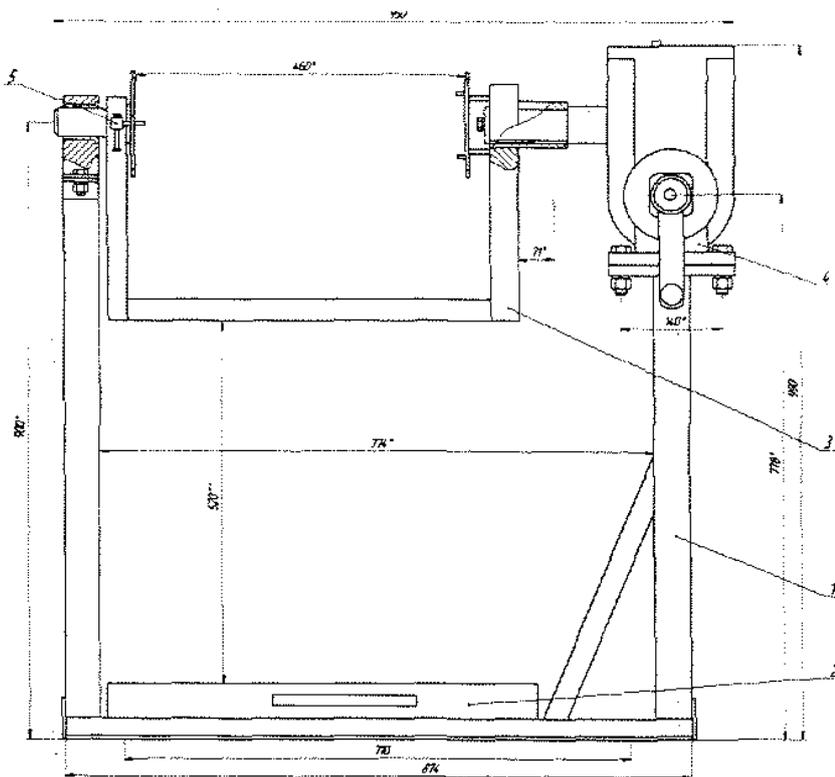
Стенд для разборки-сборки коробок передач:
